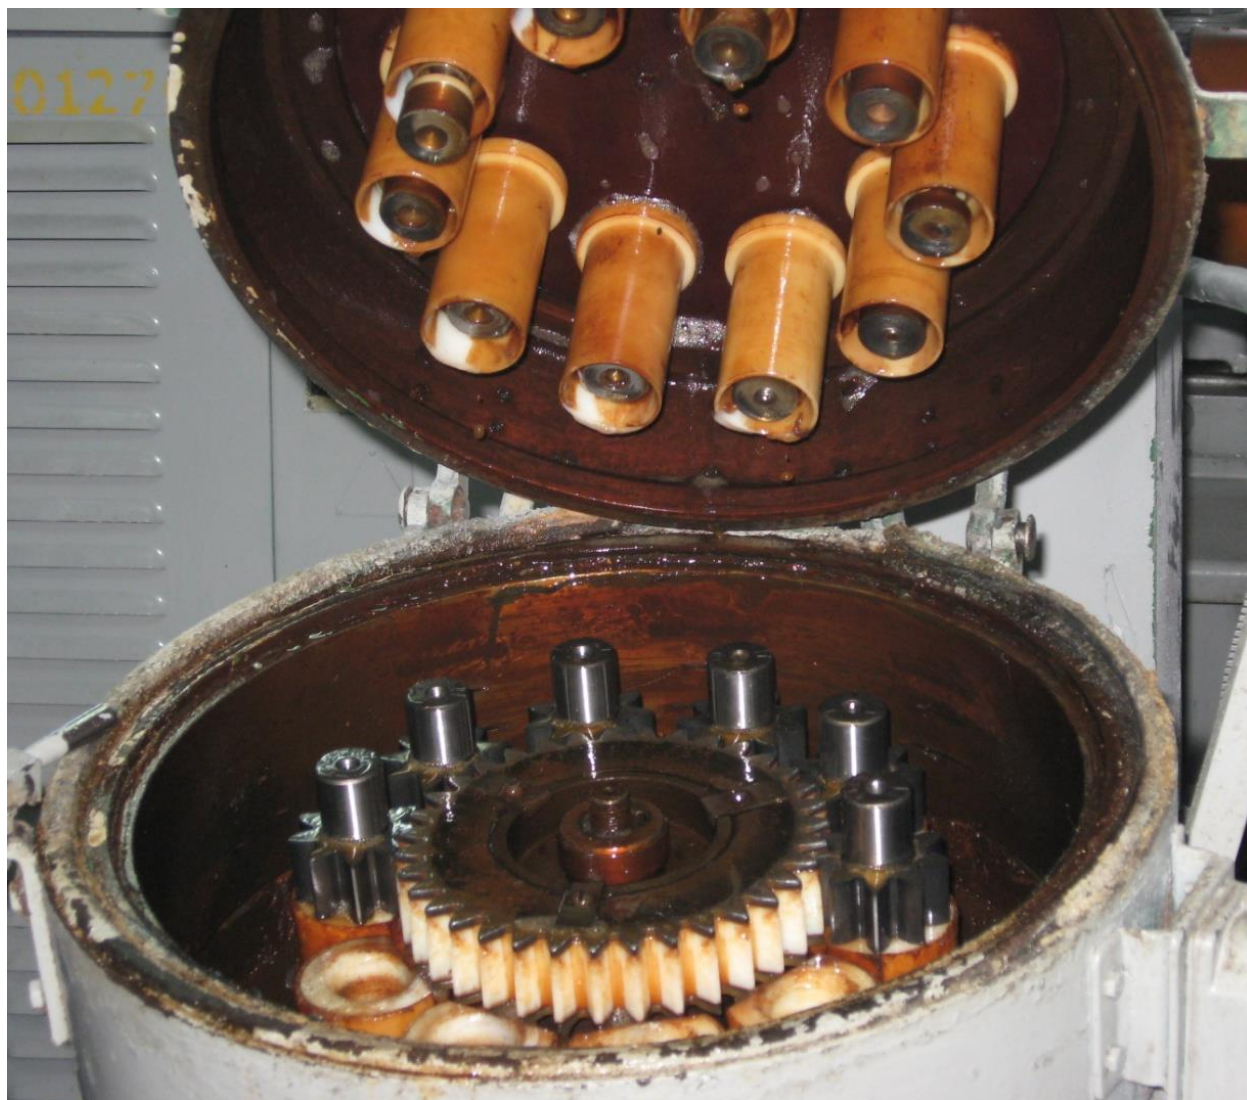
Загальний вигляд електрохімічної установки для обробки шестерні ведучої НШ-100-3-03.
